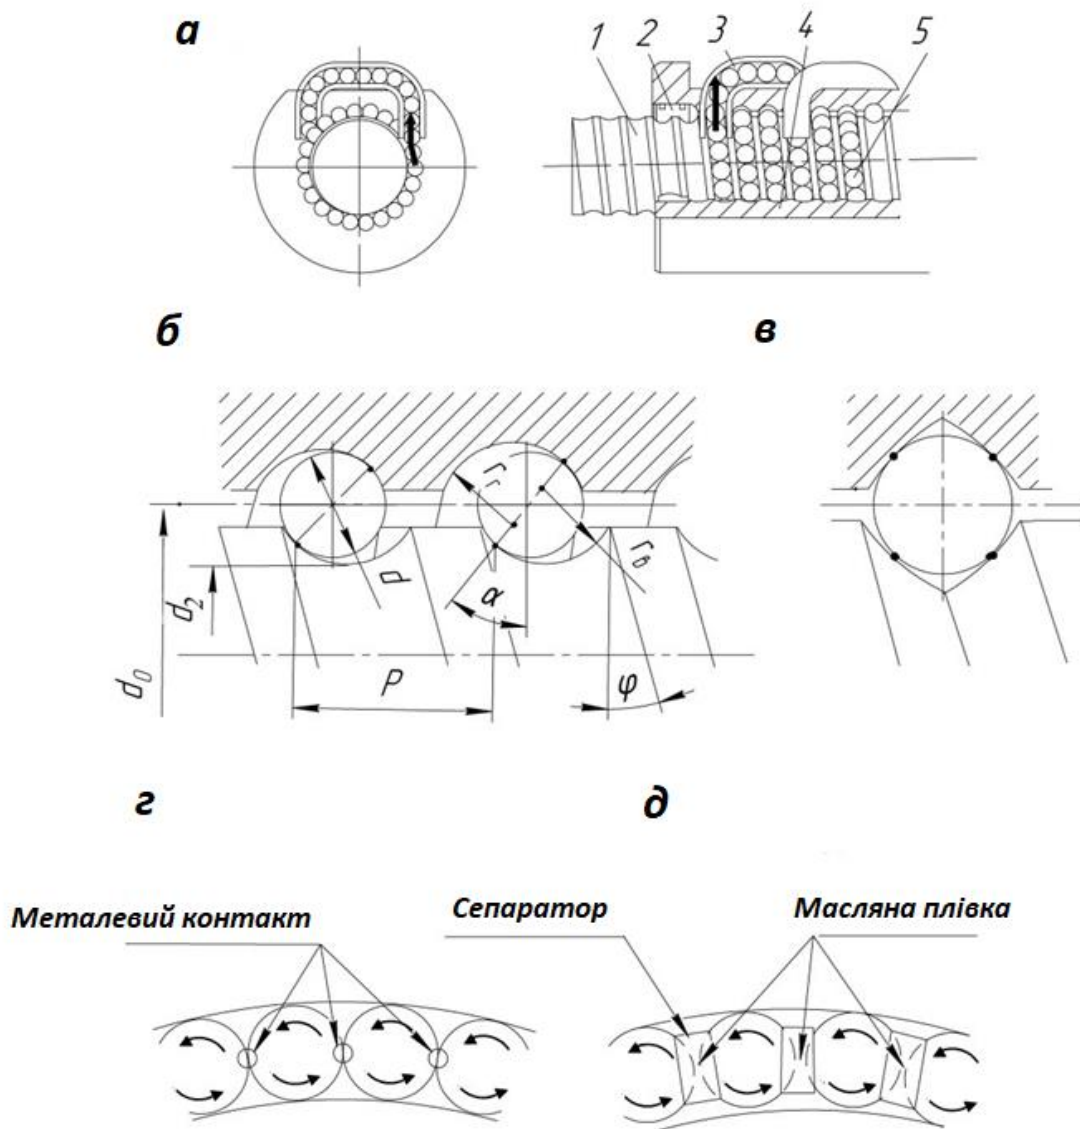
Схема кулько-гвинтової передачі.
